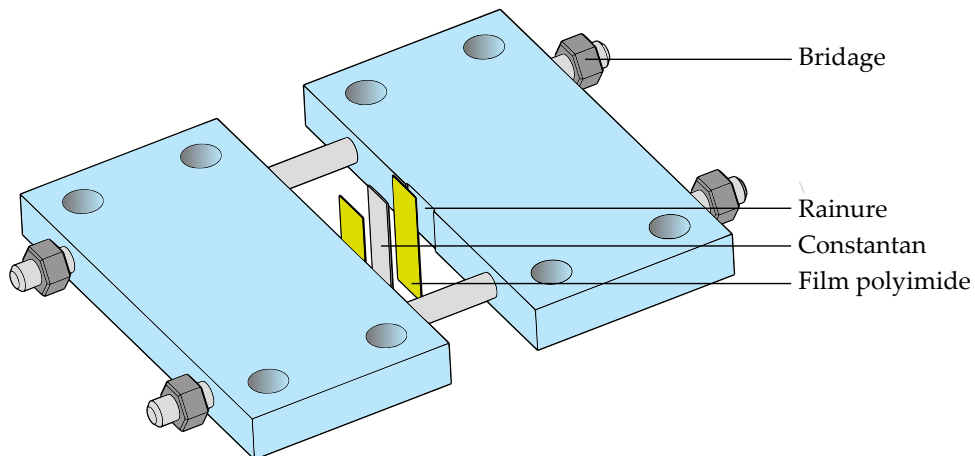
Vue éclatée du thermocouple foil.
